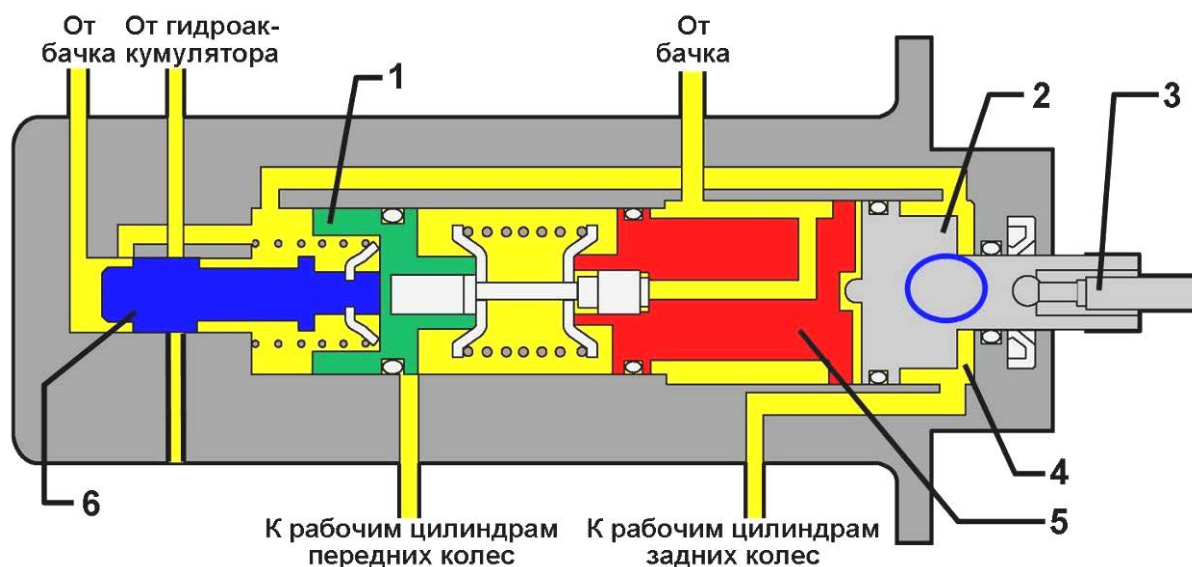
Гидравлический усилитель: 1 - поршень регулятора; 2 - поршень гидроусилителя; 3 - шток; 4 - камера усилителя; 5 - поршень главного тормозного цилиндра; 6 - золотниковый гидрораспределитель
